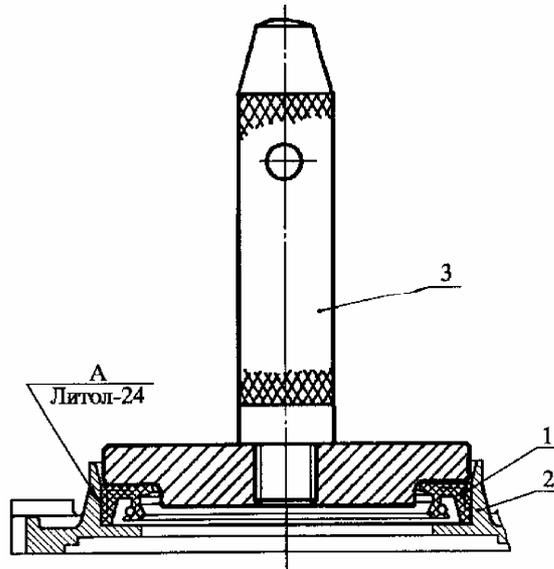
Запрессовка сальника в сальникодержатель:
